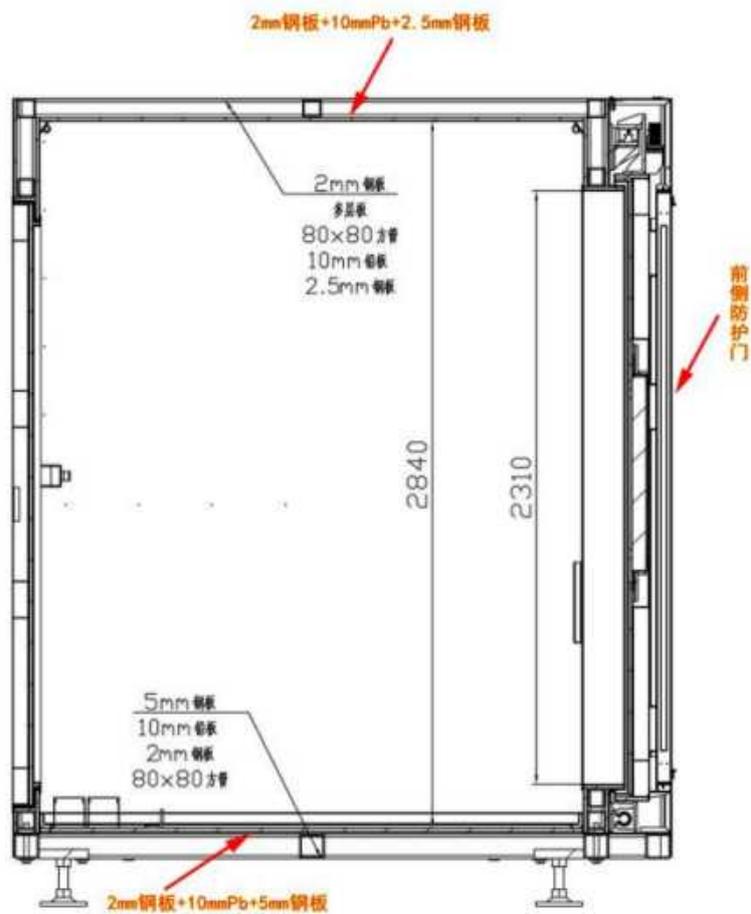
(b) 工业 CT 剖面图 (a-a 剖面)
